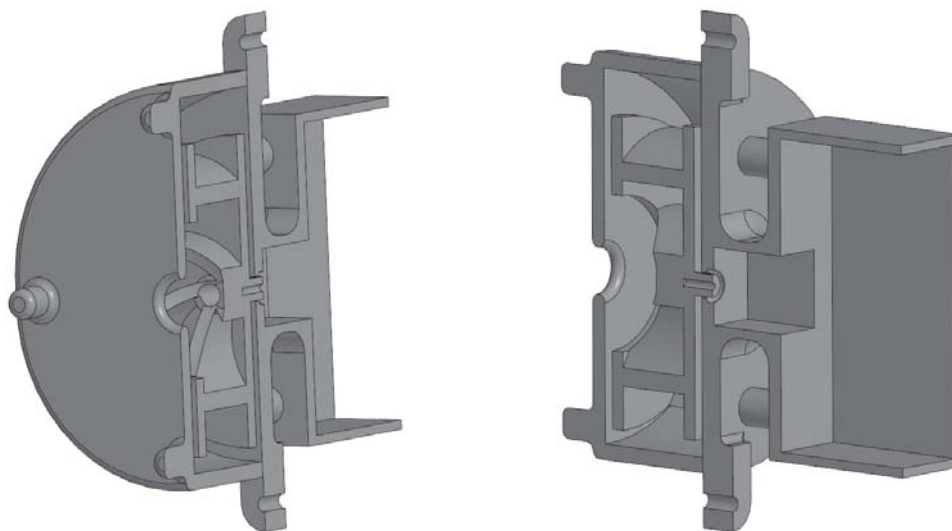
Малогабаритный центробежный насос. Вид с боку в разрезе
